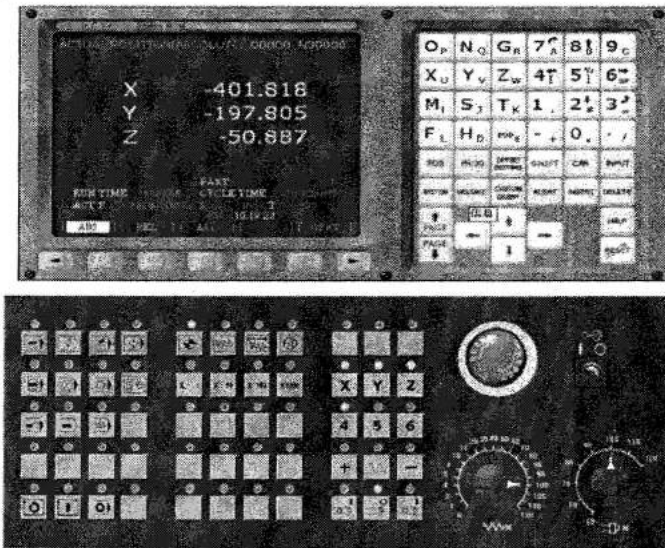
Panel kontrol CNC Sinumerik 802 S/C base line untuk mesin frais
